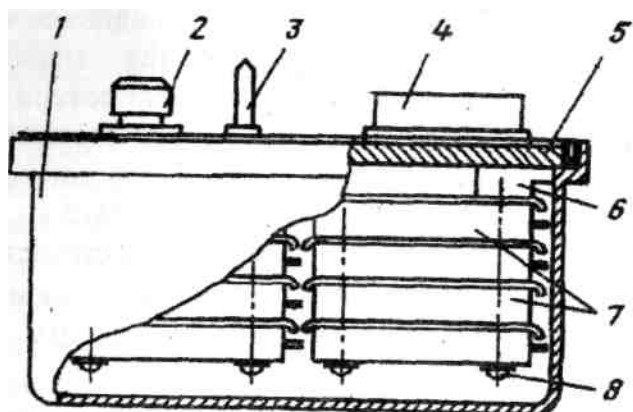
Этажерочная конструкция блока приемопередающего устройства 4-го поколения: 1 – кожух; 2 – высокочастотный разъем с полиэтиленовой заглушкой; 3 – трубка-штенгель; 4 – низкочастотный разъем; 5 – крышка-основание; 6 – бобышка; 7 – субблоки; 8 – стяжной винт
